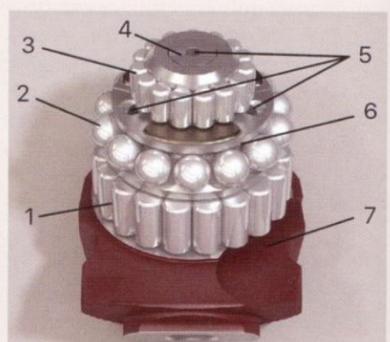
Система опоры шарошечных долот: 1 – внешний роликовый подшипник; 2 – шарикоподшипник; 3 – внутренний роликовый подшипник; 4 – поднятник; 5 – воздушные каналы; 6 – торцевой подшипник скольжения; 7 – щелевое отверстие для выпуска воздуха.
